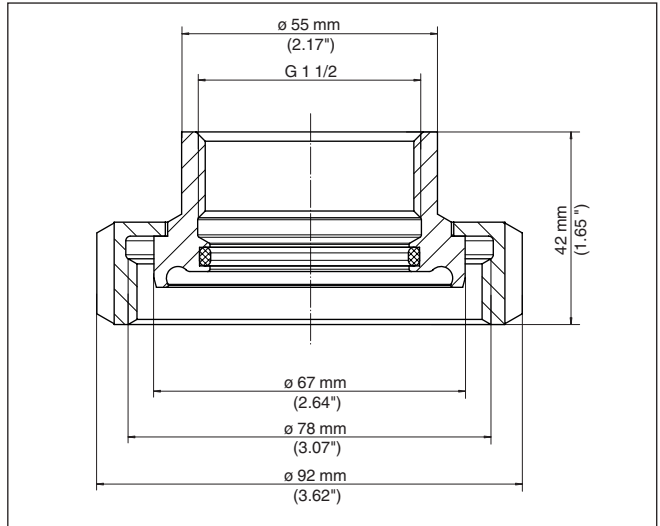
Maße Gewindeadapter G1½ (DIN 3852-X) auf Rohrverschraubung DN 50 (DIN 11864-1) PN 16
